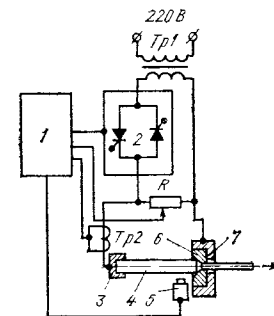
Тиристорное устройство для автоматического регулирования режима нагрева заготовки трубы при волочении
